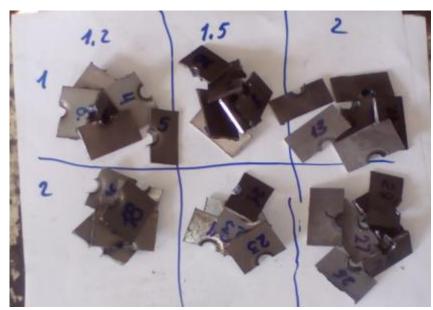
Распиленные заготовки для дальнейшего измерения геометрических параметров
